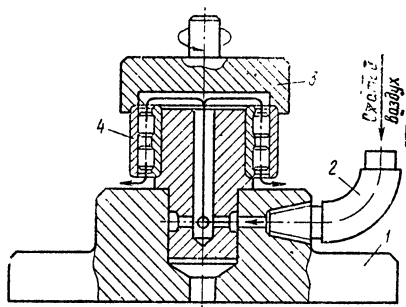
Приспособление для обдувки сборочной единицы:
